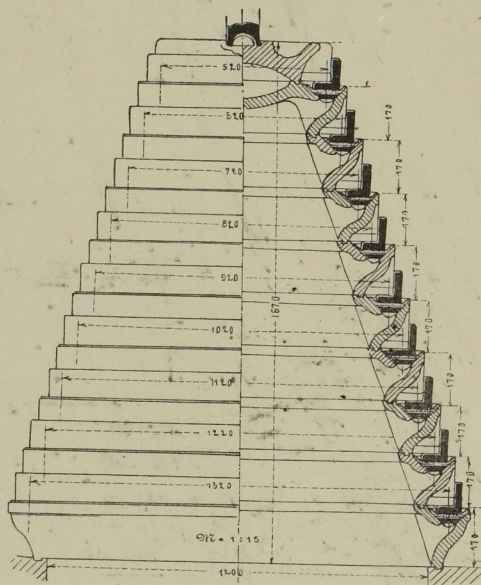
Saugventil der Hamburger Pumpe. Masst. 1:25.
